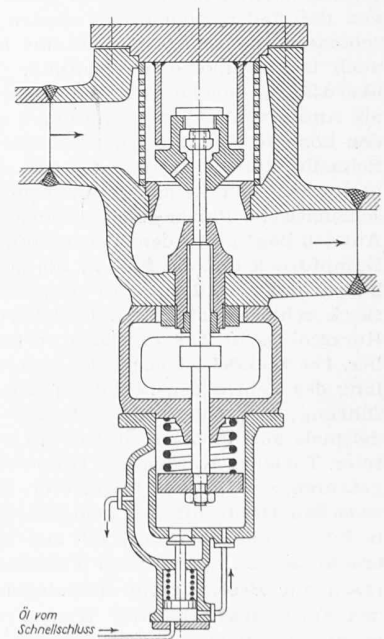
Amerikanische Bauart des Schnellschlussventils. Die Spindel ist auf der Unterseite des Kegels durch das Gehäuse nach aussen geführt. Ein Absatz der Spindel dichtet im geöffneten Zustand den Leckdampfaustritt ab
